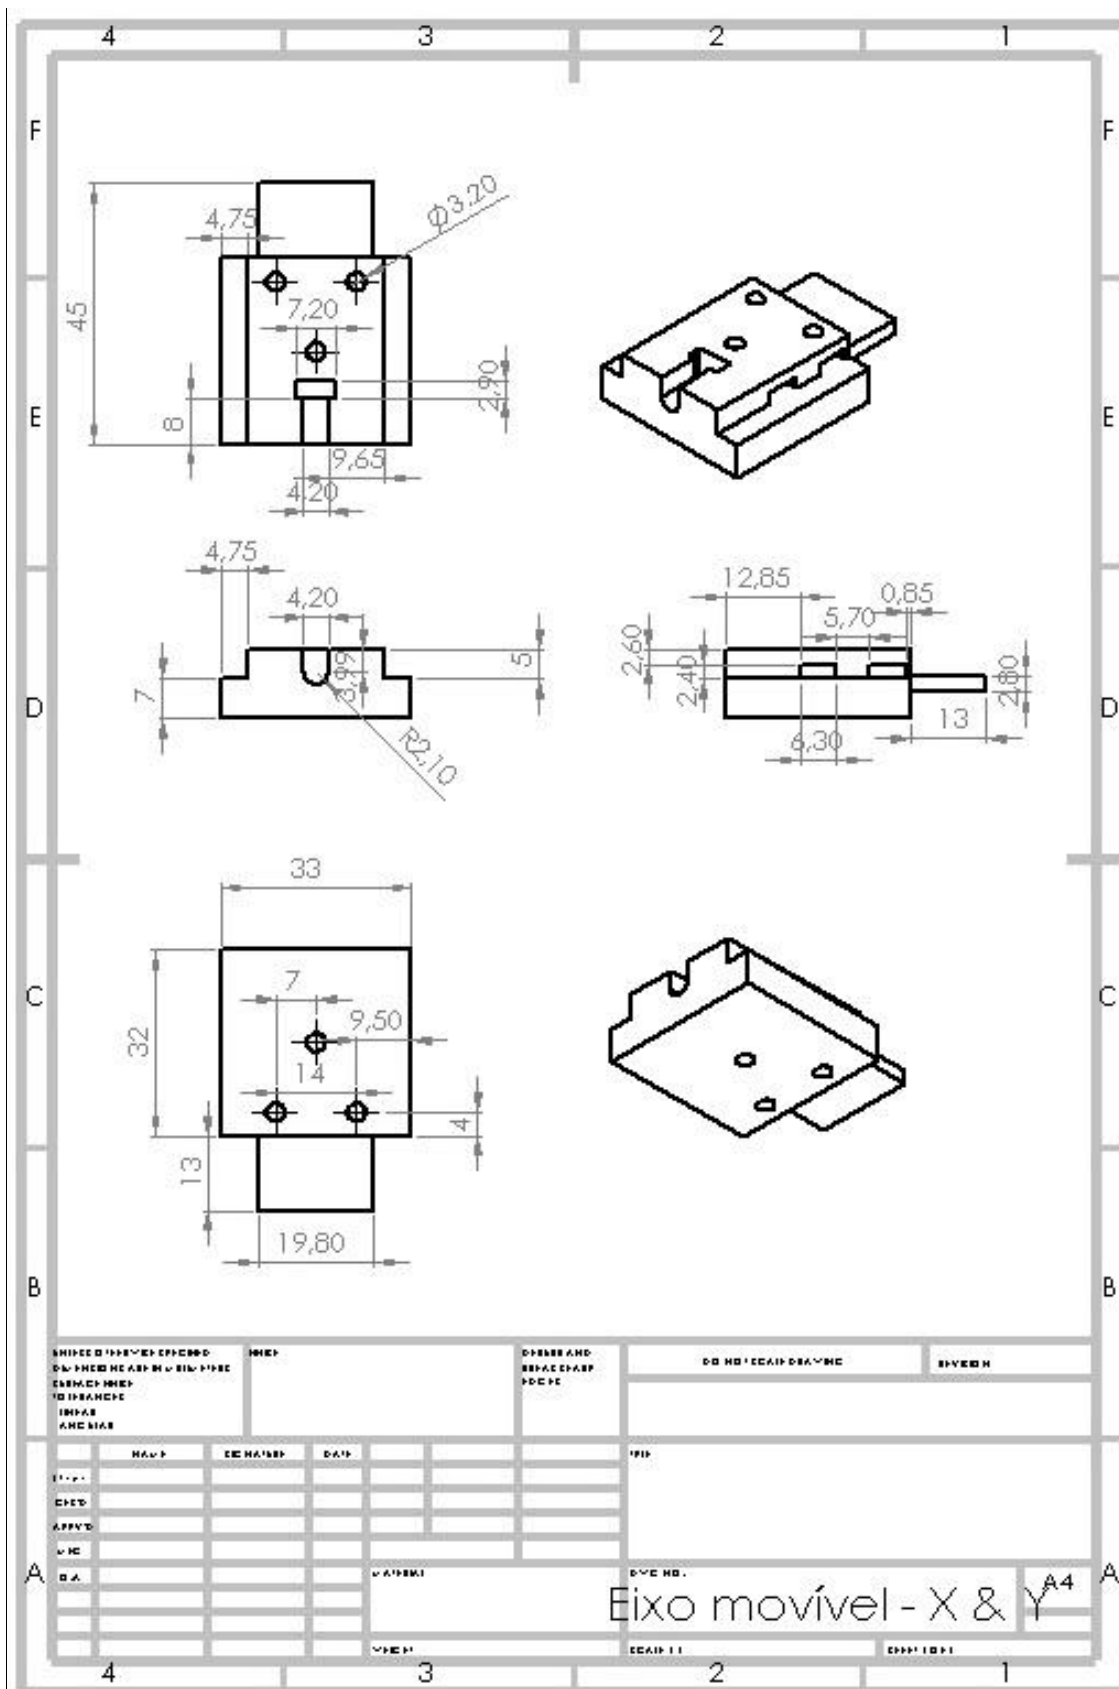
Desenho técnico da peça Eixo móvel - X & Y.
